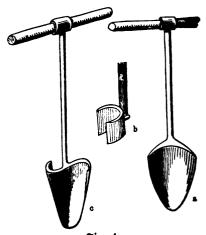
a Schippenbohrer; d Hohlbohrer; c Spiralbohrer.
